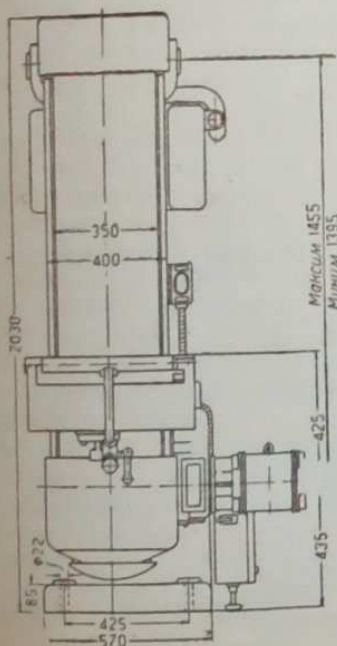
Шлифовально-ленточный вертикальный станок с неподвижным столом.
